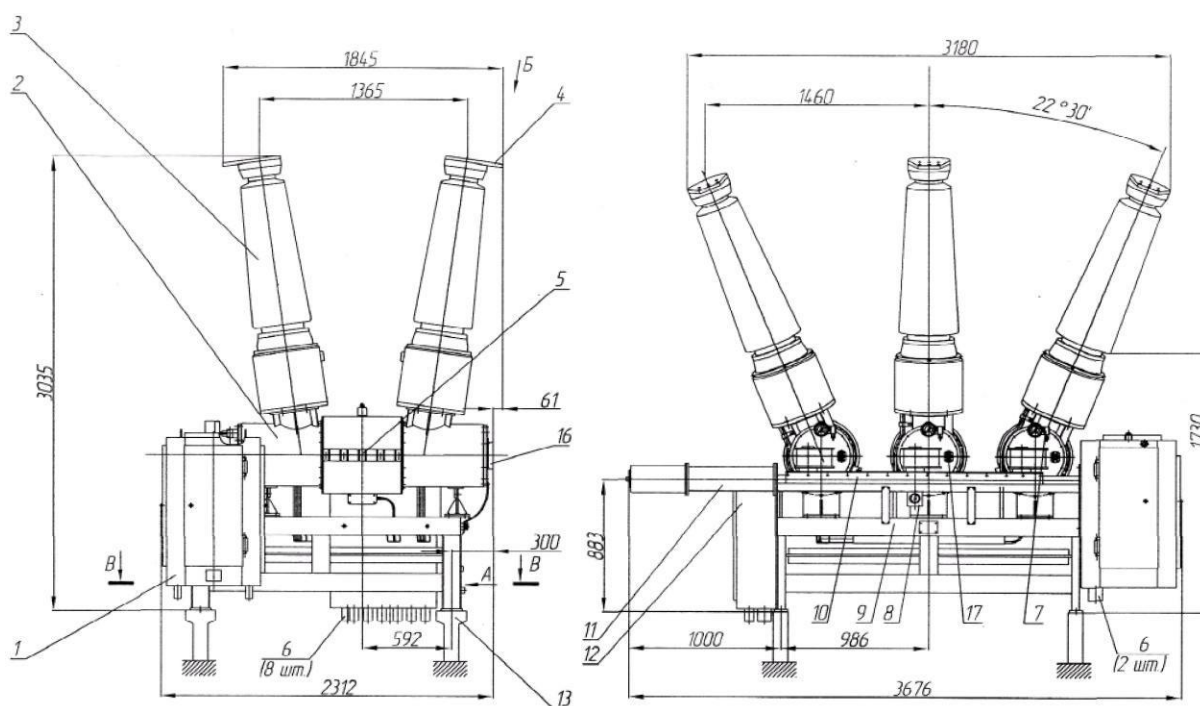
Габаритные, установочные и присоединительные размеры
